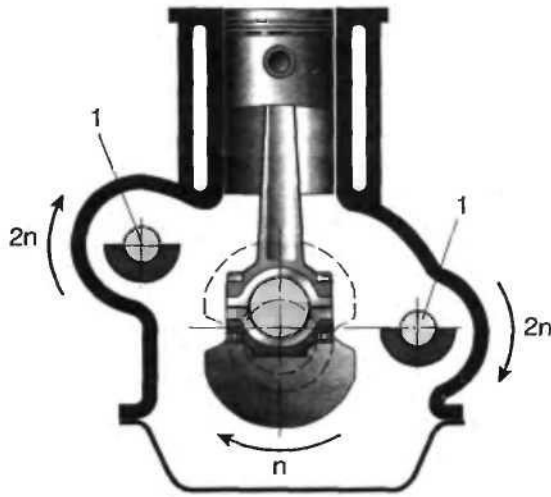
Установка балансирних валів рядного чотирициліндрового двигуна: 1 - балансирні вали
